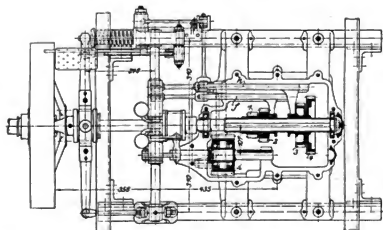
Horizontalschnitt durch Daimler-Getriebe mit angebauter Kupplung, ältere Ausführung. (Schaltung nach dem Mehrfach-Hebelsystem).
